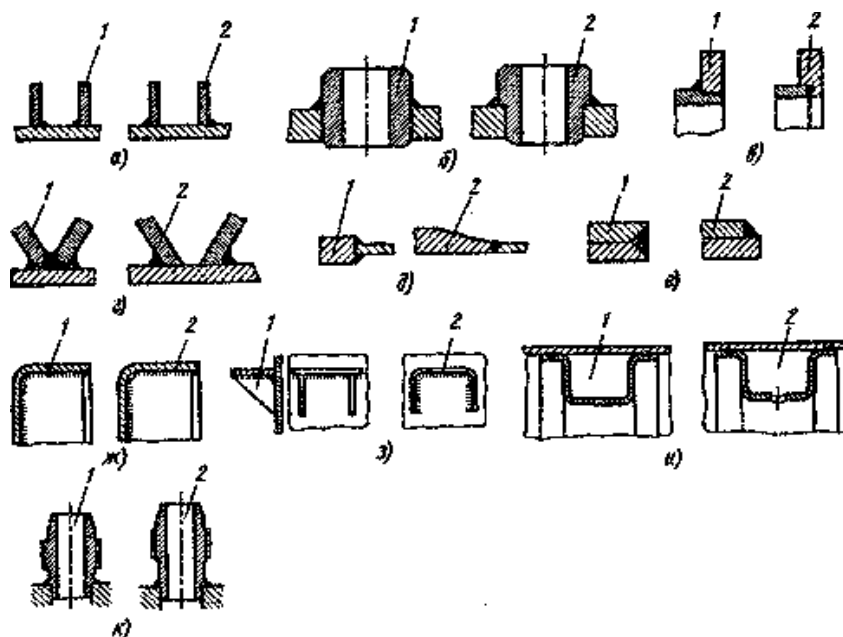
Примеры повышения технологичности конструкций сварных соединений:
